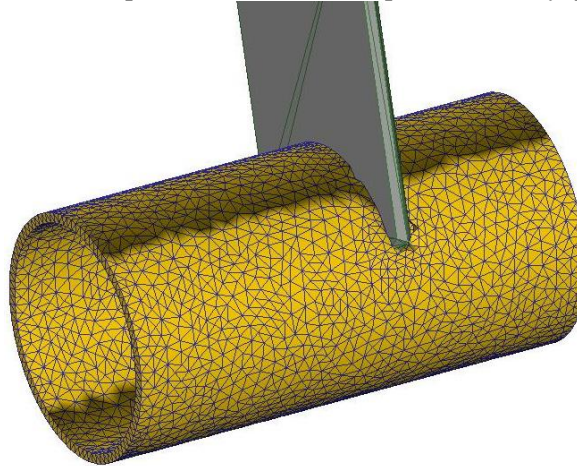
Розрахункова схема розділення труби фігурним ножом
